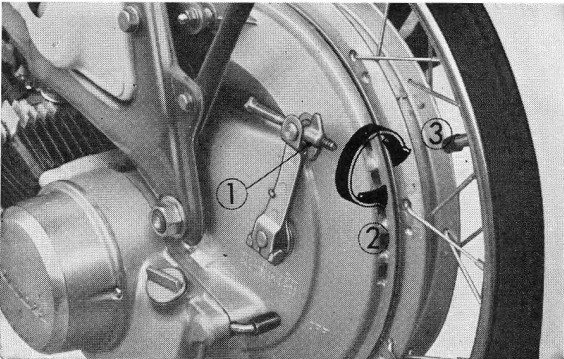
① écrou de réglage ② pour augmenter la garde ③ pour diminuer la garde
